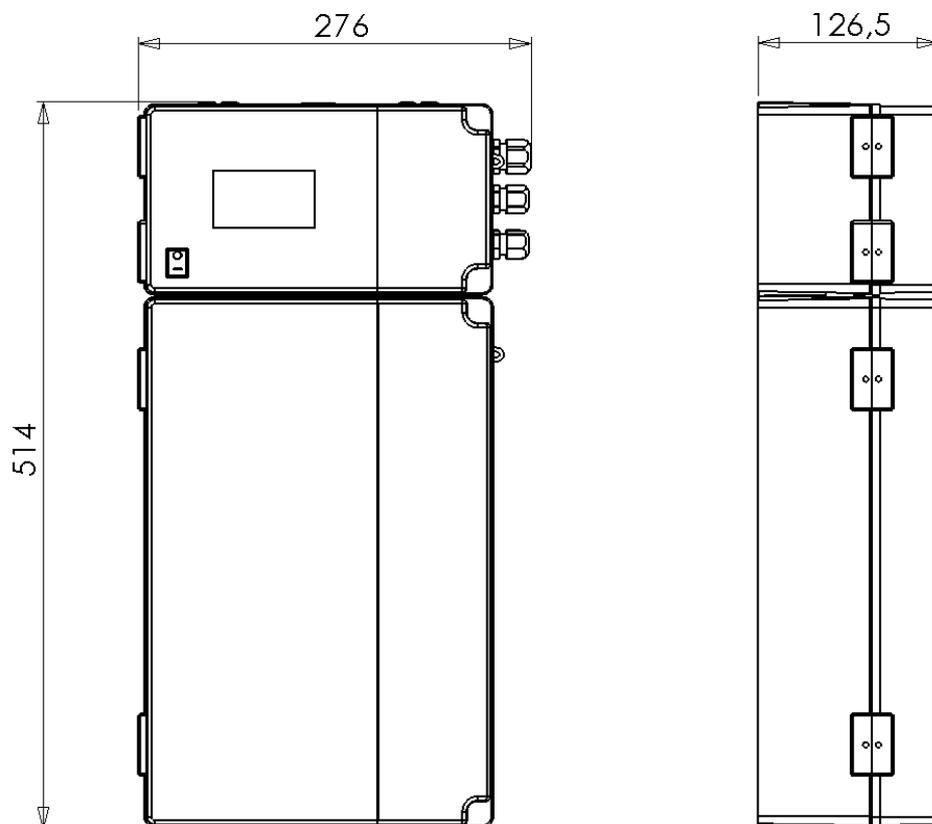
Dimensiones y posición del dispositivo montado en la pared
